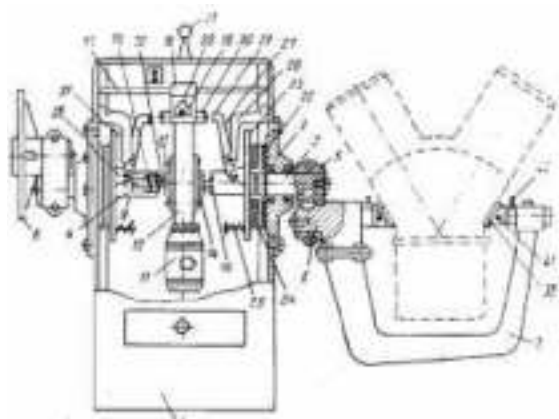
Стенд для разборки и сборки агрегатов автомобилей
